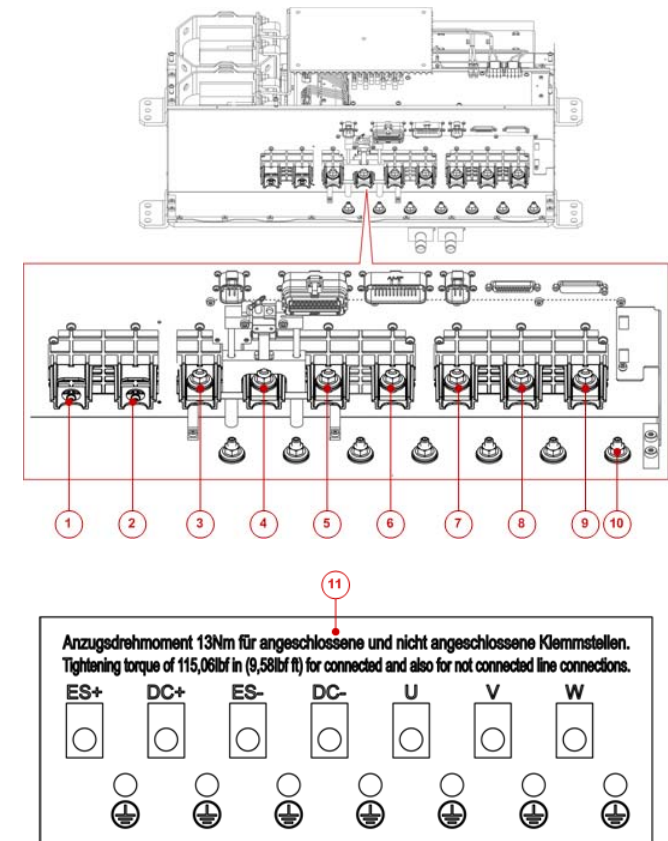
Leistungsanschlüsse und Bezeichnungen im Klemmenkasten / Power connection and denominations in the terminal box
